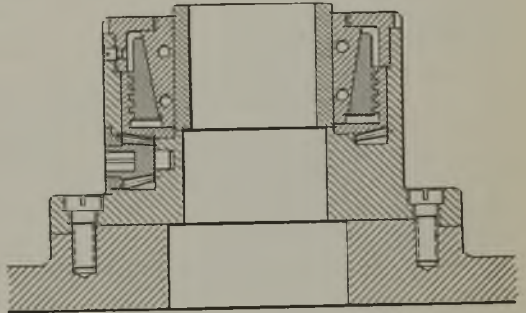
Einspannvorrichtung für eine Muffengewindeschneidmaschine.
